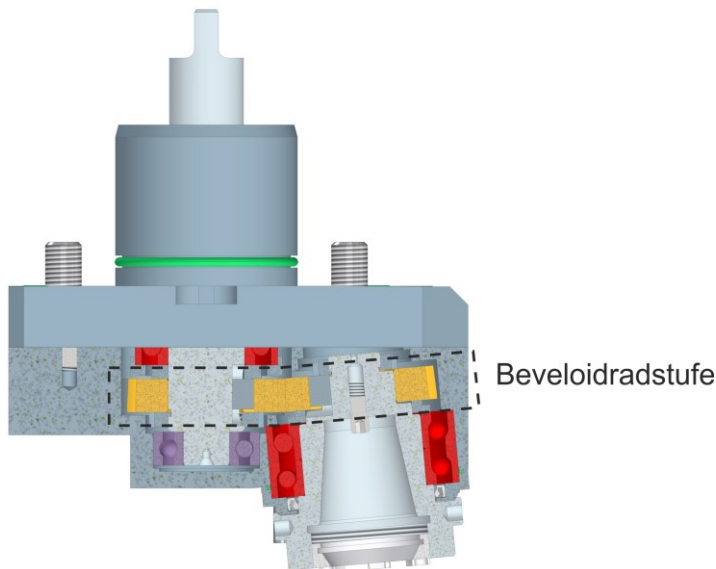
Beveloidradstufe in Werkzeughalter für Werkzeugmaschine [EWS18]
